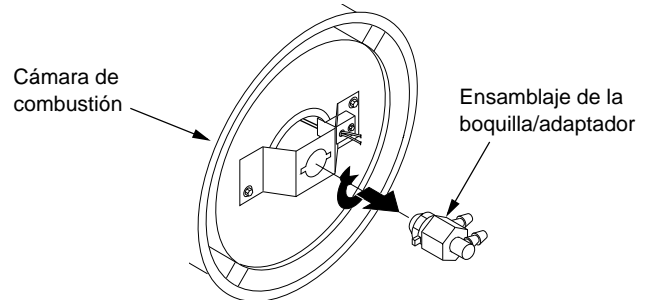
Desmontaje del ensamblaje de la boquilla/adaptador
